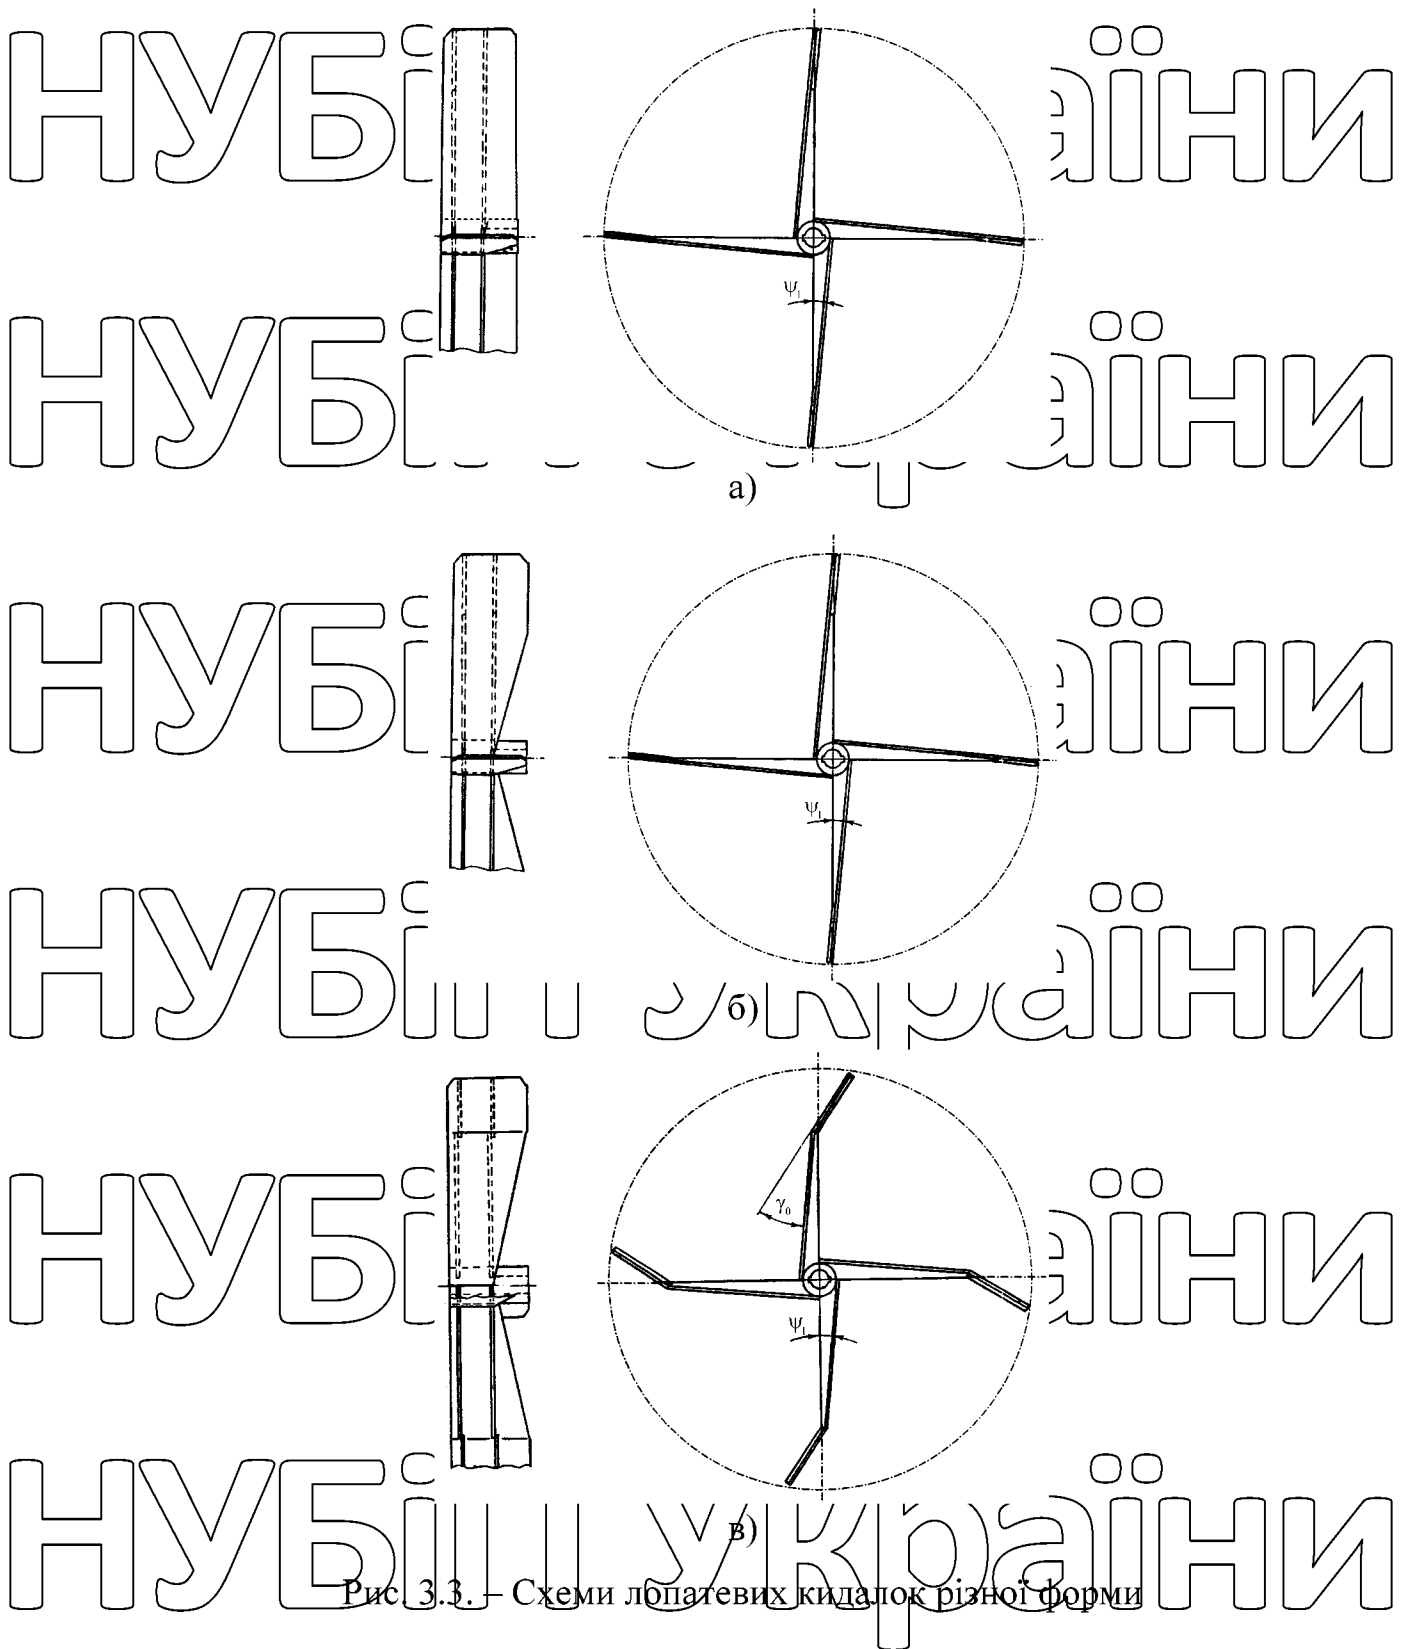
Схеми лопатевих кидалок різної форми
